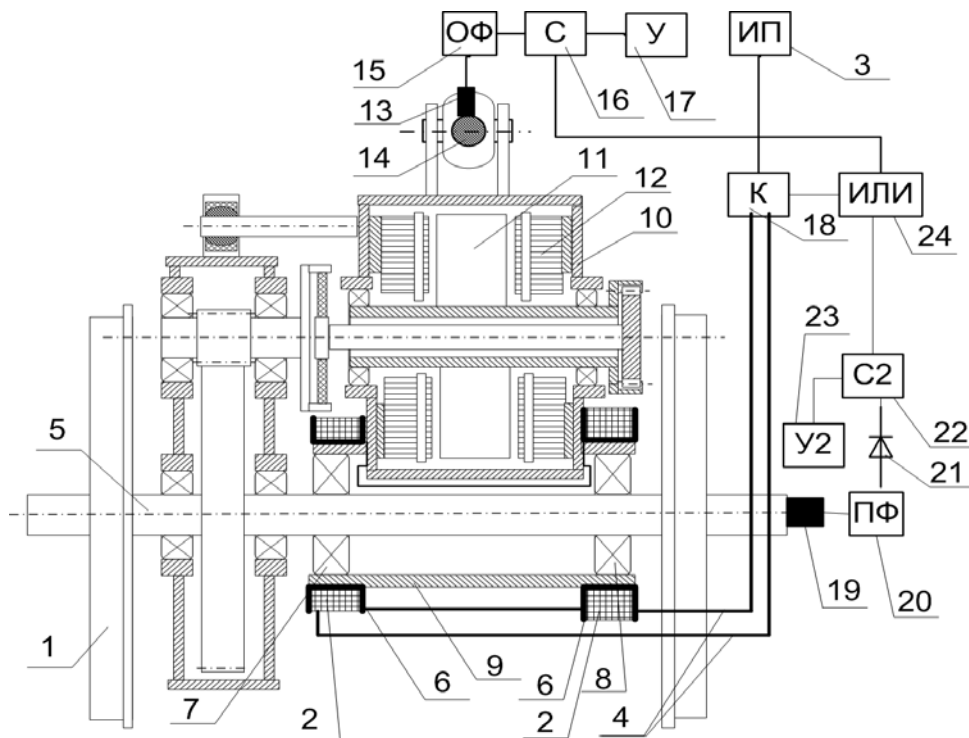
Устройство для увеличения сцепления ведущих колес с рельсами
